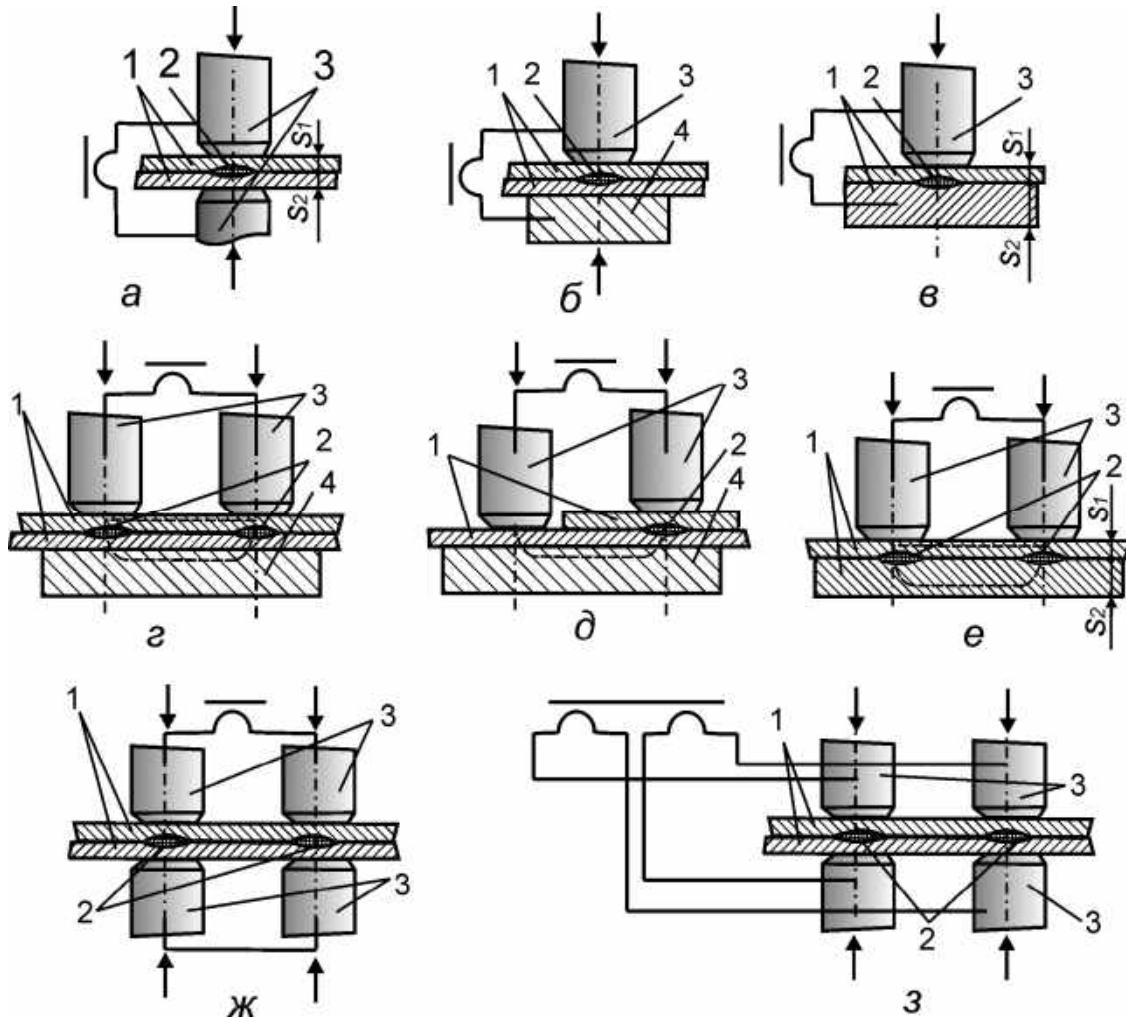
Способи контактного точкового зварювання: а – двостороннє односточкове; б, в – одностороннє односточкове; г, д, е – одностороннє двоточкове; ж, з – двостороннє двоточкове; 1 – деталі, що зварюються, 2 – зварні точки, 3 – електроди, 4 – підкладка
